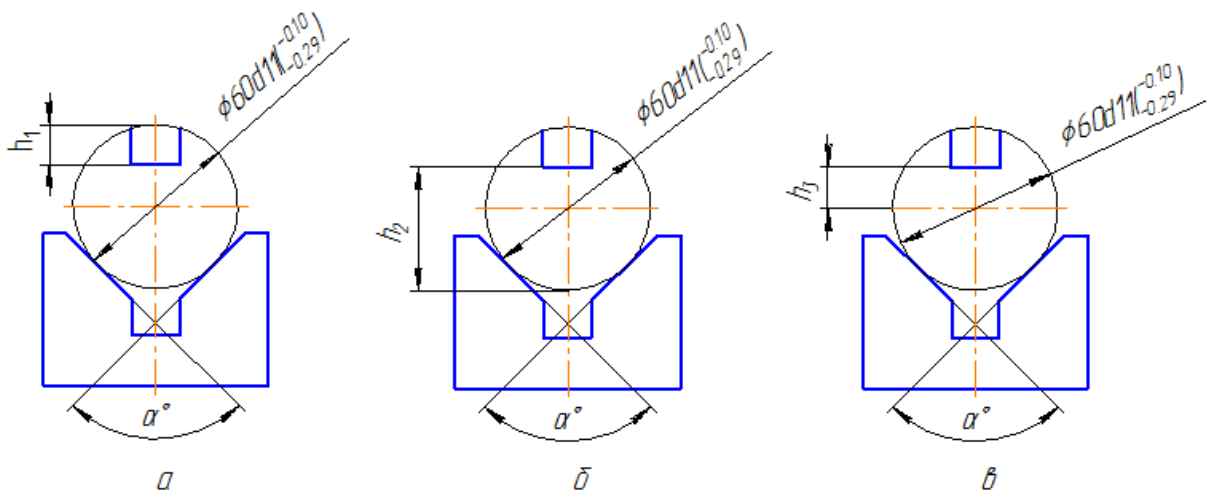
Установка цилиндрической детали в призму для обработки шпоночного паза (три способа задания глубины шпоночного паза: а) от верхней образующей; б) от нижней образующей; в) от оси вала)
